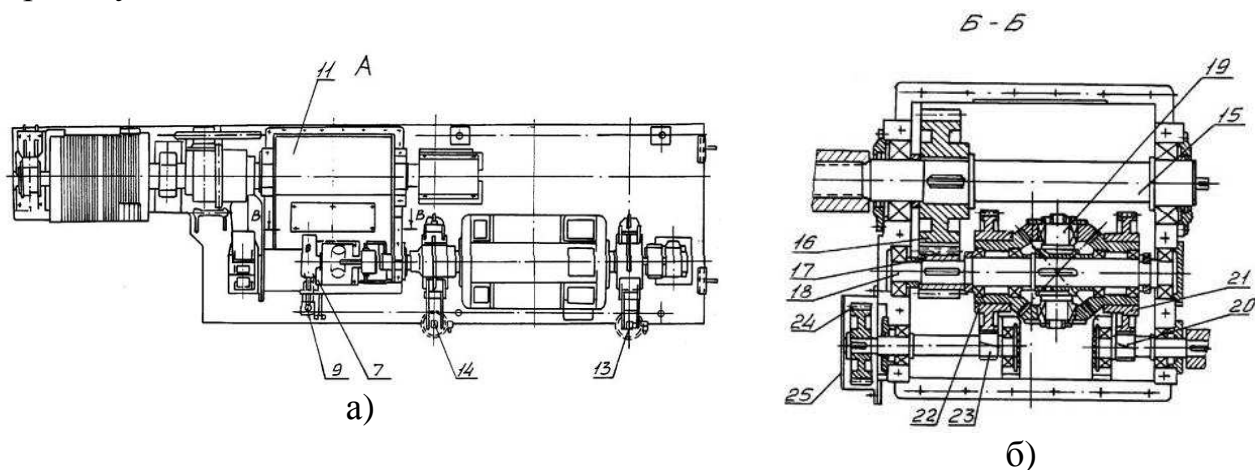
Вид привода фурмы машины (а), выходной вал дифференциального редуктора (б)
